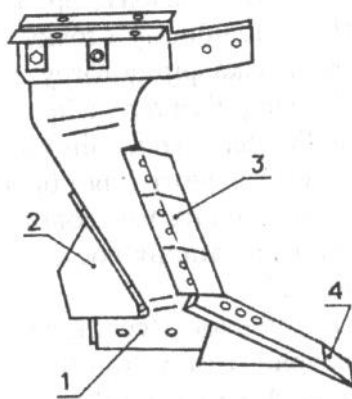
Корпус плуга Paraplow: 1 - польова дошка;
